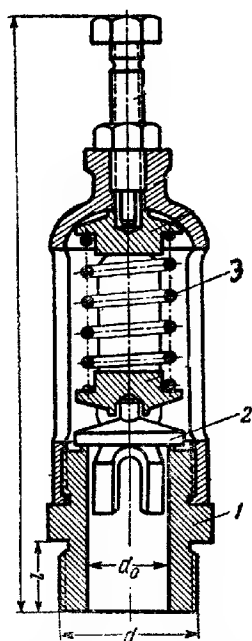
Пружинный предохранительный клапан с упорным регулировочным болтом и боковыми окнами для выпуска пара
